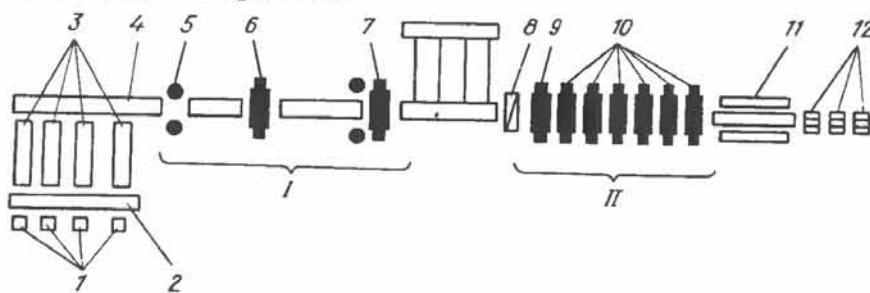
Схема расположения оборудования полунепрерывного широкополосного стана 2800/1700:
